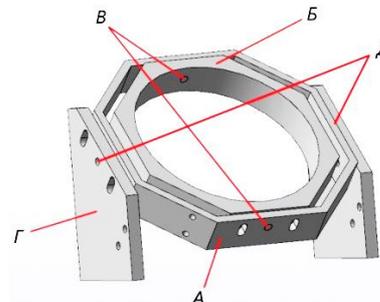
3D-модель корпуса зеркала: А — обойма юстировки зеркала по вертикальной плоскости; Б — обойма юстировки зеркала по горизонтальной плоскости; В и Д — осевые втулки крепления; Г — основная стойка корпуса зеркала
